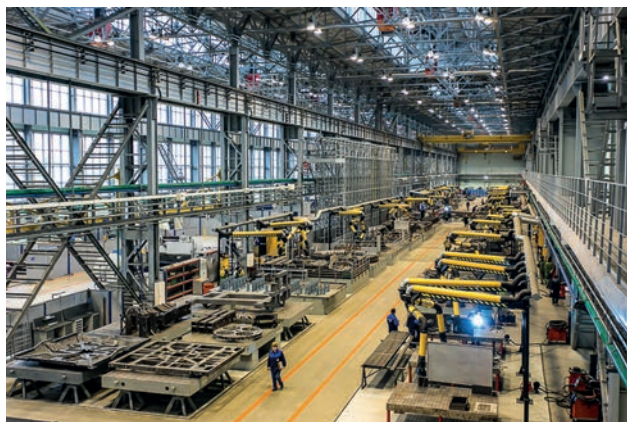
Сварочный цех АО «ГОЗ Обуховский завод»
